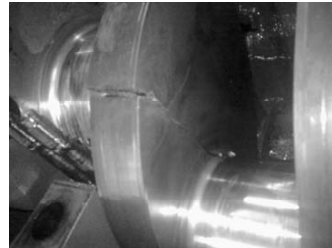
Вид щеки коленчатого вала двигателя ГЧН25/34 после поломки
